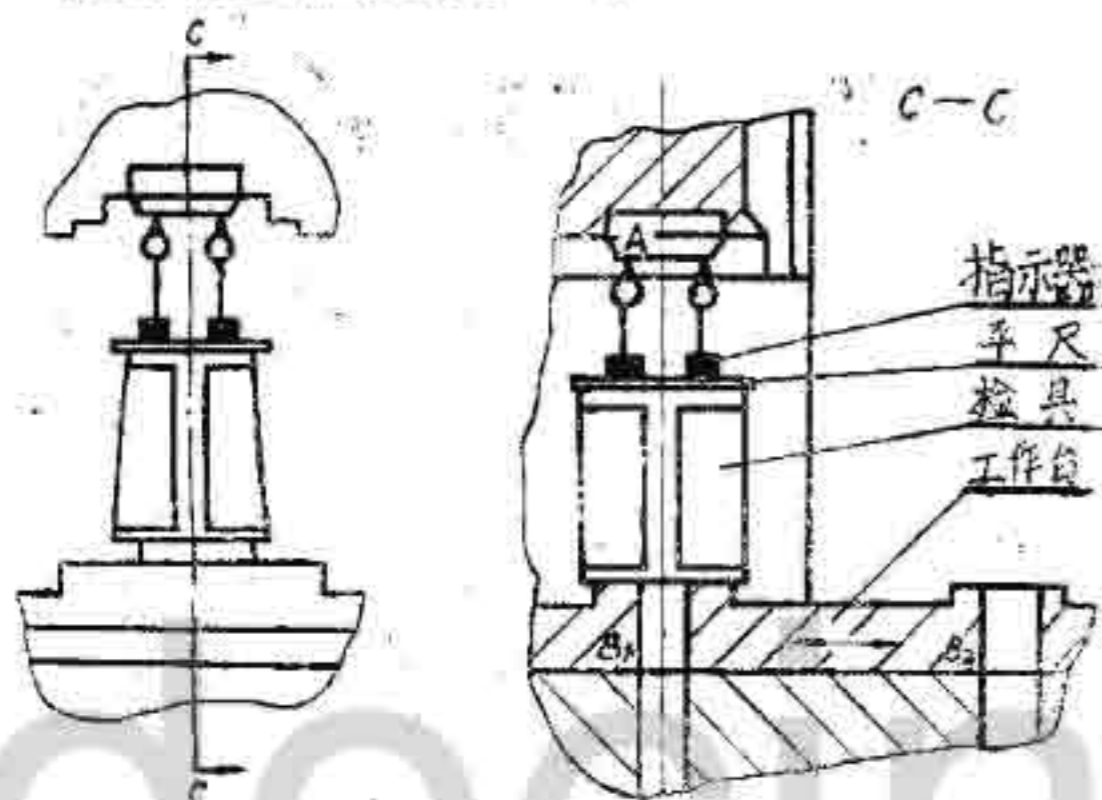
检验冲垫下平面与工作台上平面的平行度
